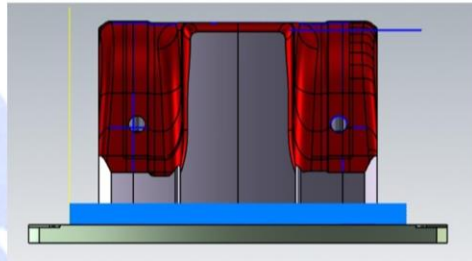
Autocad 2D Floor Shifter CF Tampak Atas
